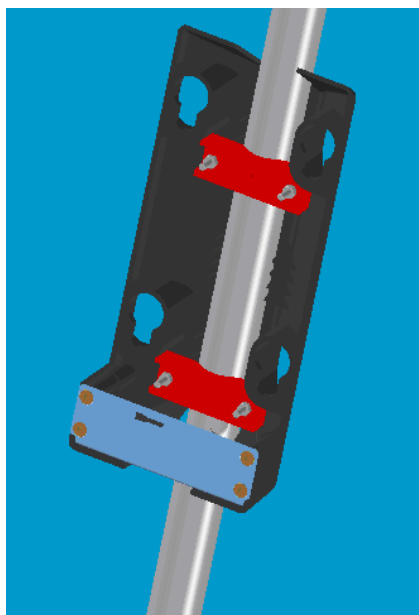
Vista particolare collarini di fissaggio staffa VTX-UC
